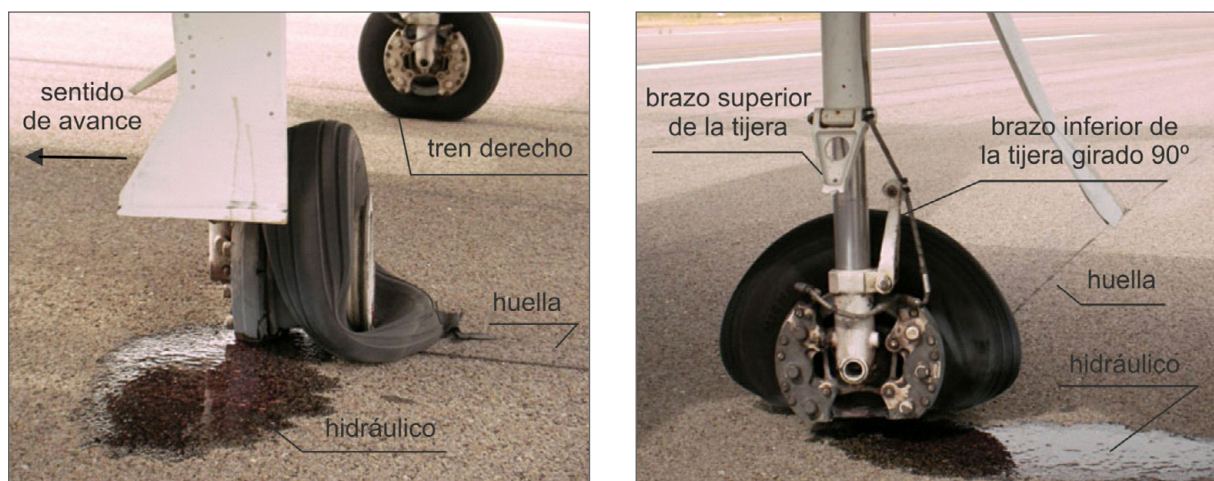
Vistas lateral izquierda y frontal del tren principal izquierdo
